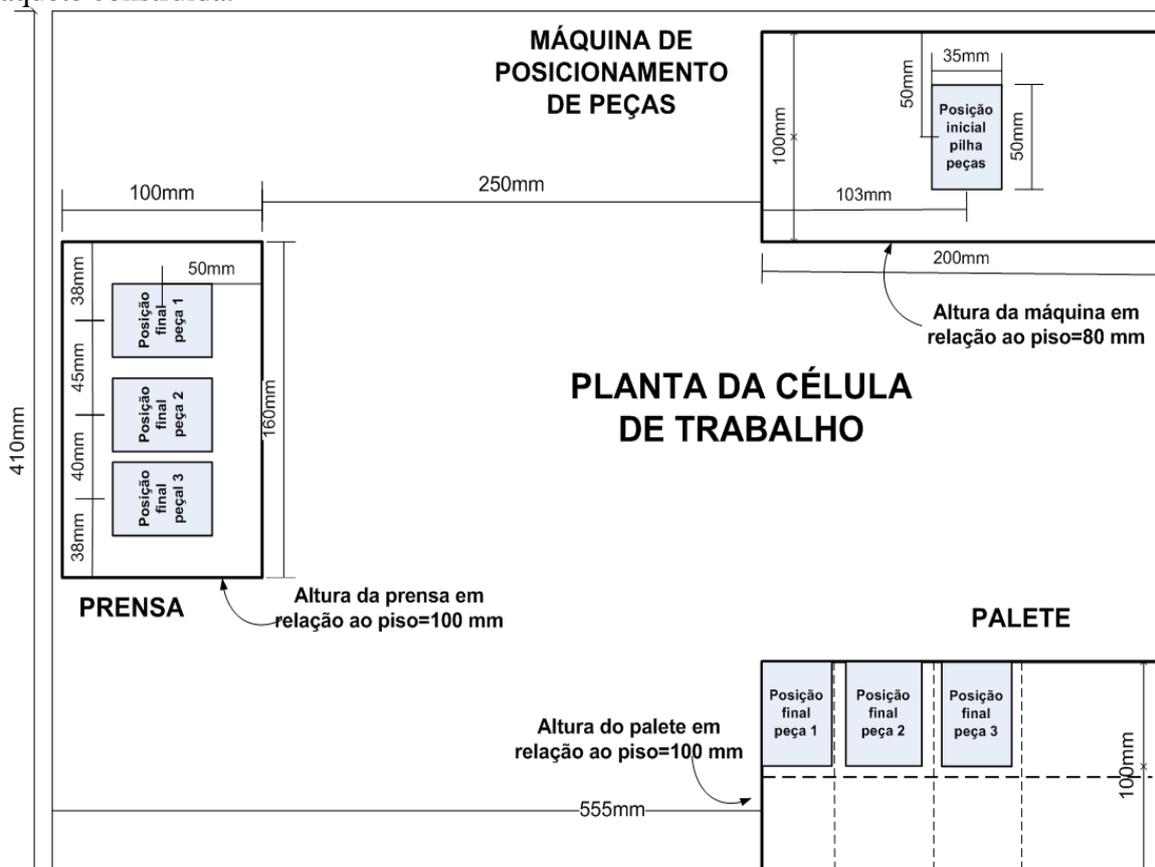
Planta da célula de trabalho, com as dimensões e posições das peças.
